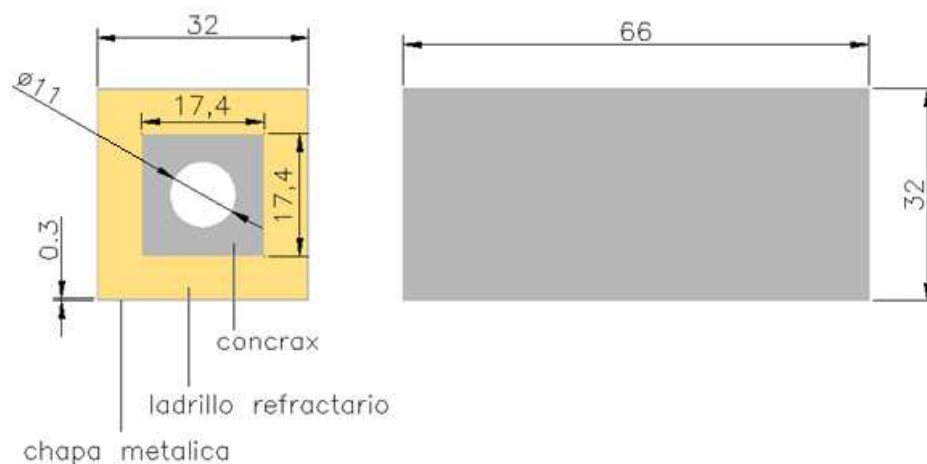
Dimensiones de la cámara de calentamiento (medidas en cm)
